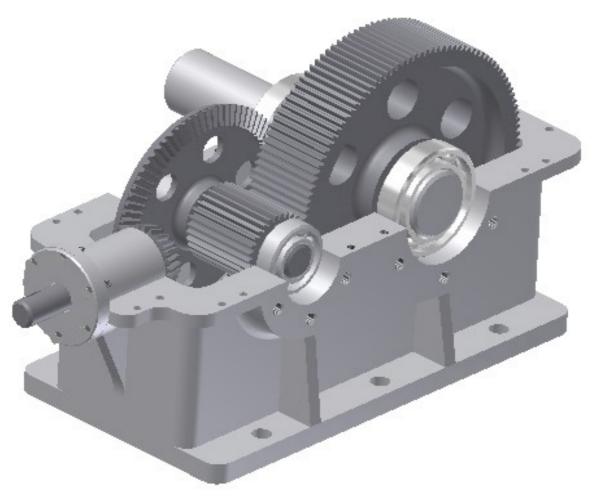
Трехмерная модель сборки редуктора (без крышек)
